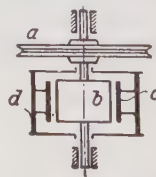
Esquema del mecanismo de transporte y del dispositivo tensor: a, rodillo del cable para el avance de éste; b, rotor del electromotor; c, sistema magnético giratorio del motor; d, tambor tensor.
